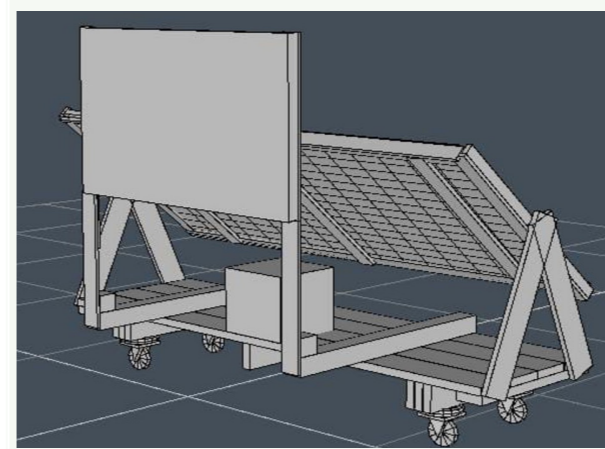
Modelo tridimensional da instalação do quadro branco.
